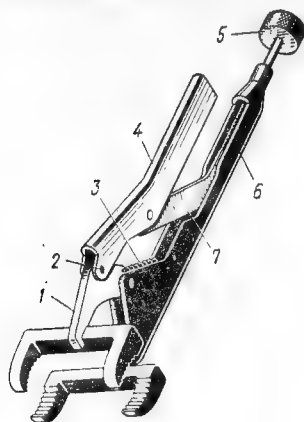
1 — корпус; 2 — винт регулировочный; 3 — ручка; 4 — пружина; 5 — губка подвижная
